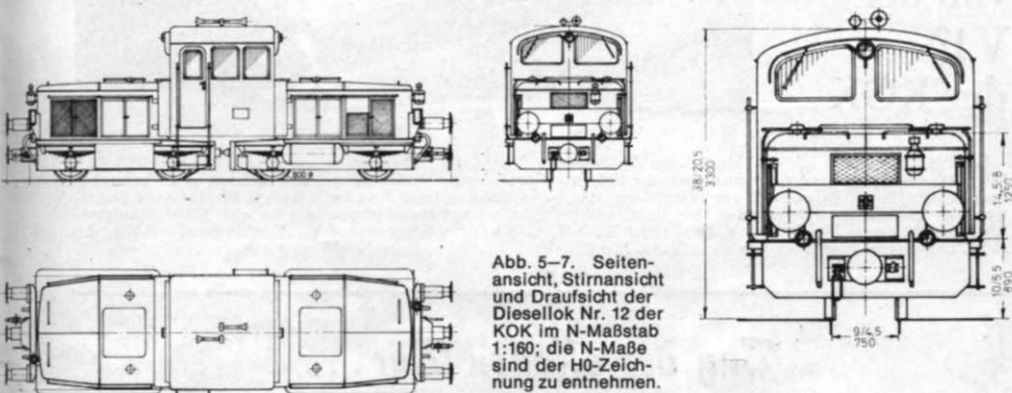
Seitenansicht, Stirnansicht und Draufsicht der Diesellok Nr. 12 der KOK im N-Maßstab 1:160; die N-Maße sind der H0-Zeichnung zu entnehmen.
